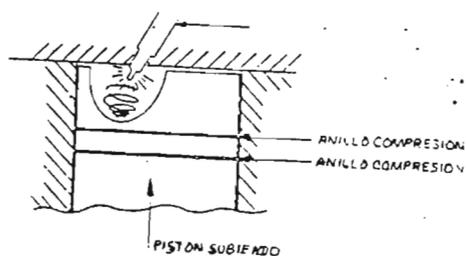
Inyección Indirecta. La inyección se hace sobre la Cámara de Combustión Maquinada en el Pistón.
